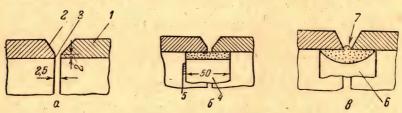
Типы сварных соединений: a — сварной V-образный стык; b — сварной стык с цилиндрическим подкладным кольцом; e — сварной стык с фасонным подкладным кольцом.
